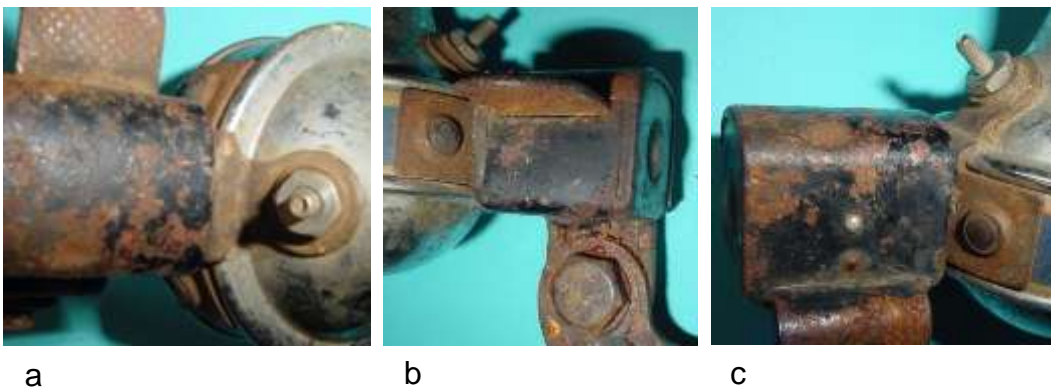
T-Flansch: a) Befestigung am Kabelanschlussbolzen, b) Nietverbindung, c) Abdeckblech mit Niet zur Befestigung der Rückstellfeder
